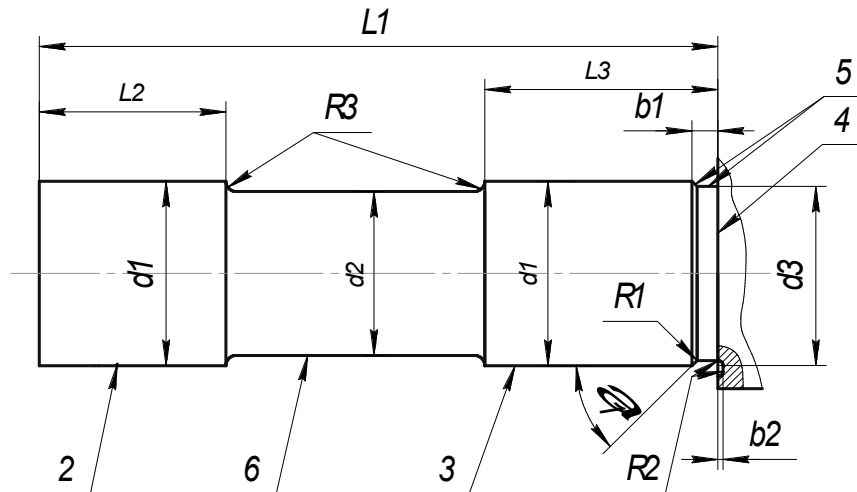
Конструкція модуля поверхонь 3МПБ312.
